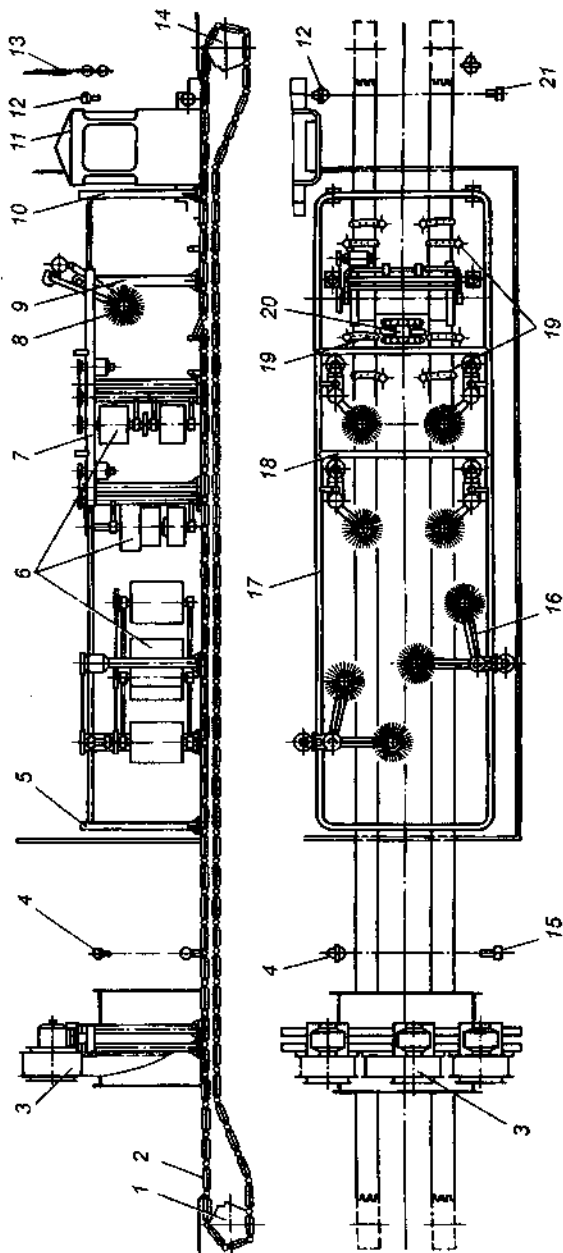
Щеточная моечная установка с автоматическим управлением: 1 — звездочка приводной станции; 2 — тяговая цепь; 3 — вентиляторы; 4, 12 — фотоэлементы; 5, 10 — душевые рамки; 6, 8 — душевые щетки; 7 — стойка; 9 — поршень; 11 — кабина оператора; 13 — светодвор; 14 — звездочка натяжной станции; 15, 21 — прожекторы; 16 — старые распашные щетки; 17, 18 — продольные и поперечные трубы; 19, 20 — устройства обмыва днища
